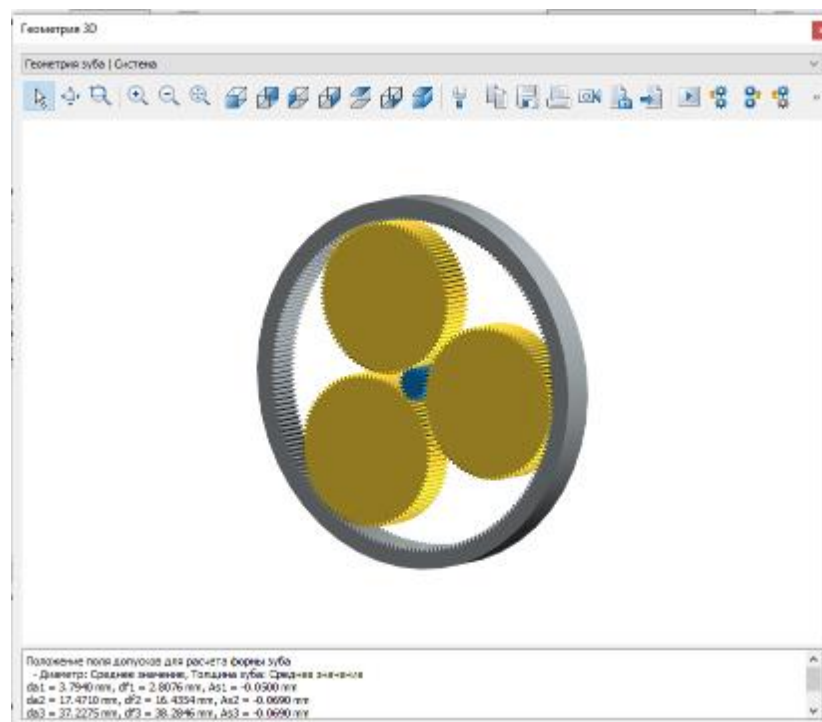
3D модель 1 ступени планетарного редуктора
